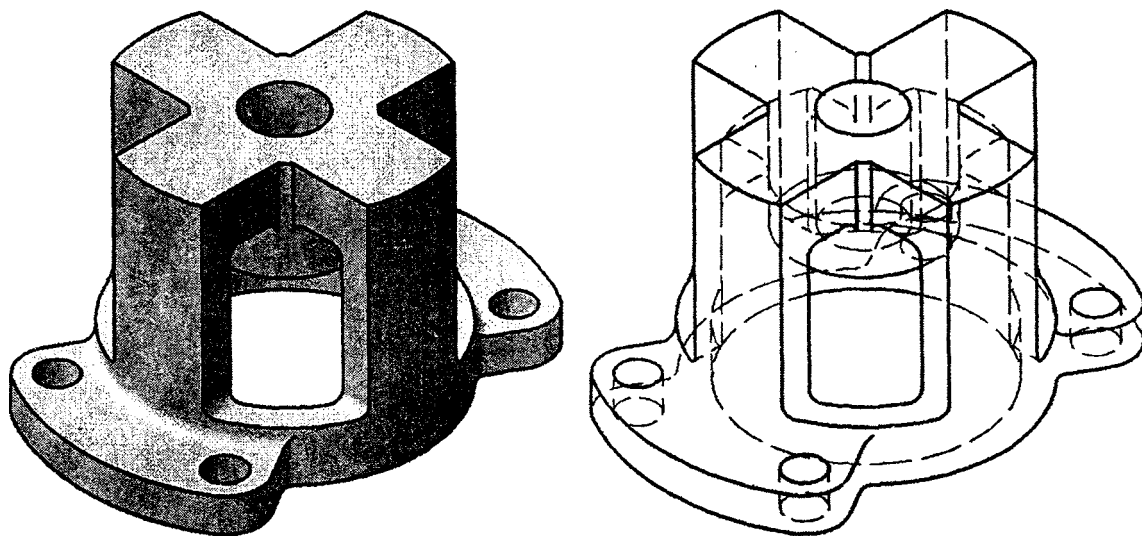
Образец детали, чертеж которой (рис. 3.14) содержит ломаные разрезы
